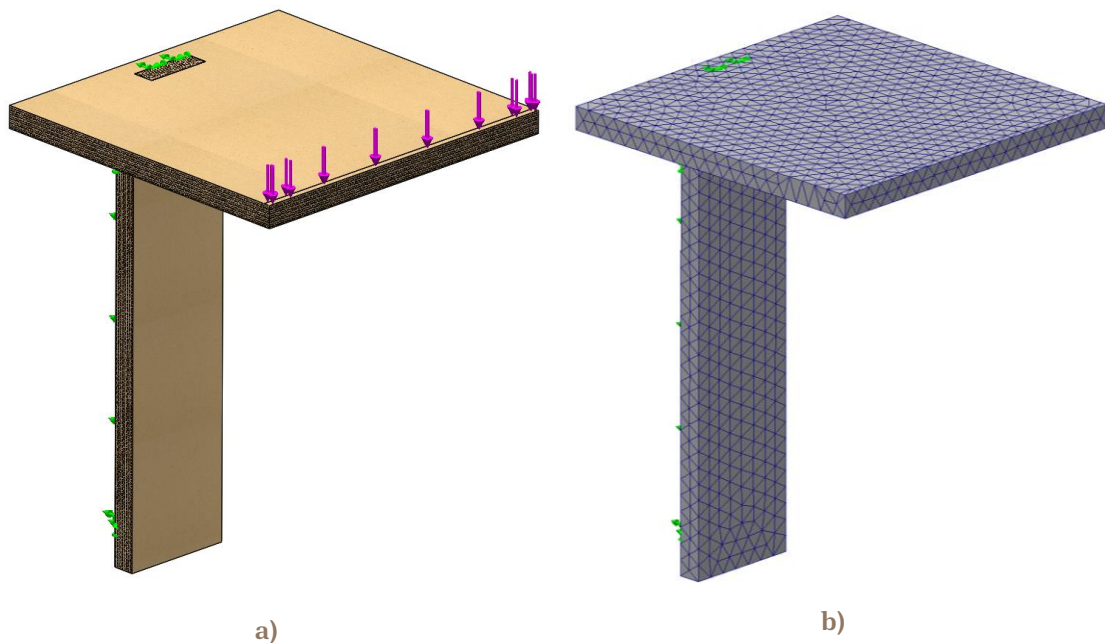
Unión plancha + vertical 1 tipo caja y espiga: a) configuración del ensayo de carga estática, b) malla generada || Fuente: Elaboración propia
